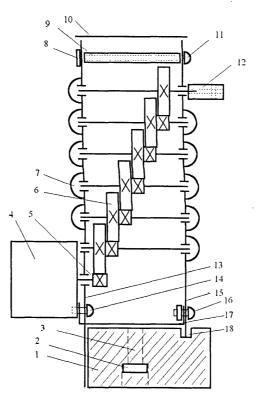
Редуктор: 1 — рейка крепления редуктора; 2 — гайка; 3 — отверстие ∅6 мм; 4 — двигатель редуктора; 5 — шестерня вала двигателя; 6 — шестерни редуктора; 7 — эпоксидные упоры валов шестерен; 8 — гайка стяжного винта; 9 — втулка стяжного винта; 10 — прижимная крышка; 11 — стяжной винт; 12 — втулка выходного вала; 13, 15 — корпус редуктора; 14 — винт крепления к корпусу двигателя и скобы; 16 — винт крепления скобы к корпусу; 17 — скоба; 18 — паз
